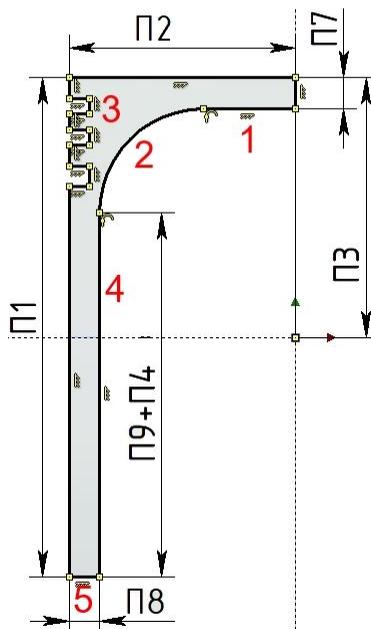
3D-профиль базовой геометрии поршня
